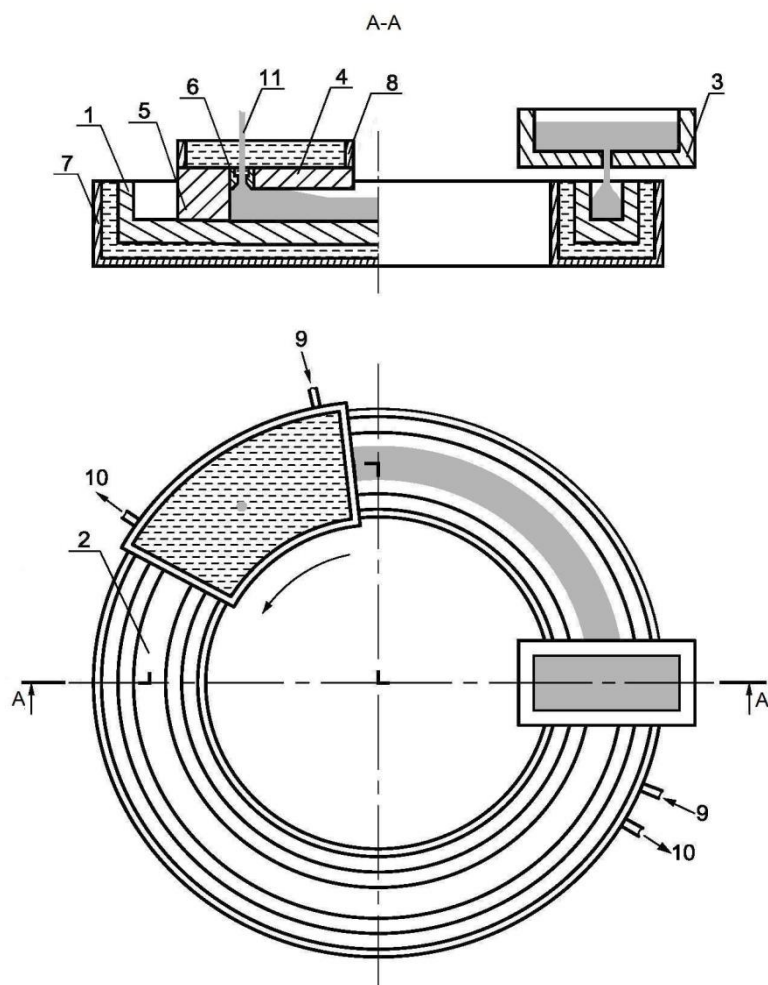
Устройство для охлаждения инструмента установки непрерывного литья – прессования [39]:
